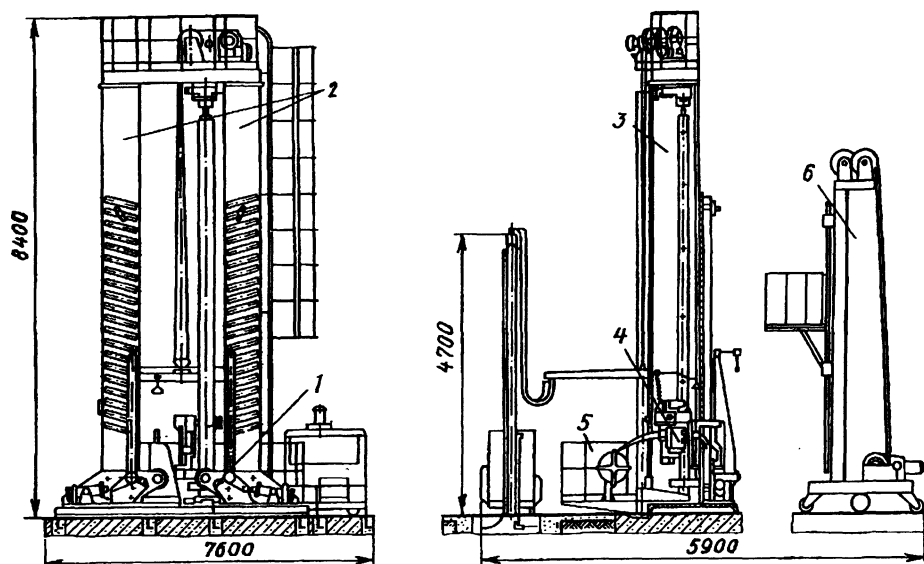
Схема типовой установки для электрошлаковой сварки прямолинейных швов
